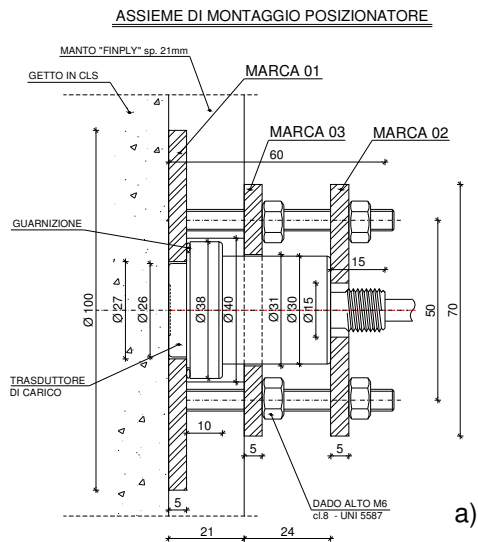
a) Dettaglio delle flange di assemblaggio dei trasduttori di pressione;
